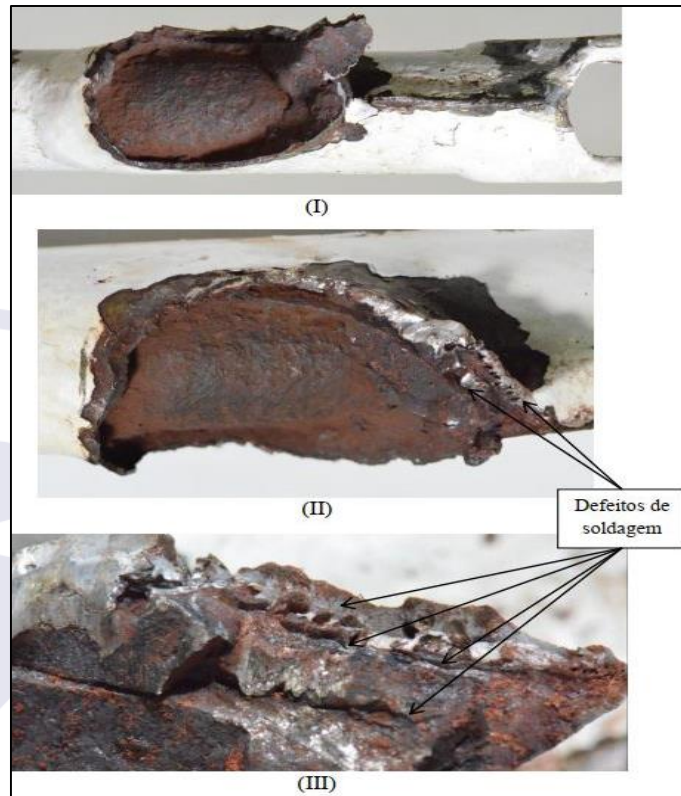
Em (I-III), a superfície de fratura do eixo da roda apresentando a presença de corrosão generalizada e defeitos de soldagem (porosidade e trincas).
